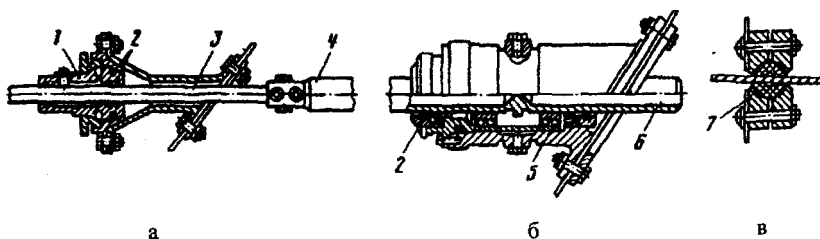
Гермовыводы: а – тяг; б – валов; в – тросов; 1 – сферический вкладыш; 2 – резиновые кольца; 3 – шток; 4 – тяга; 5 – шарикоподшипник; 6 – вал; 7 – резиновый вкладыш
